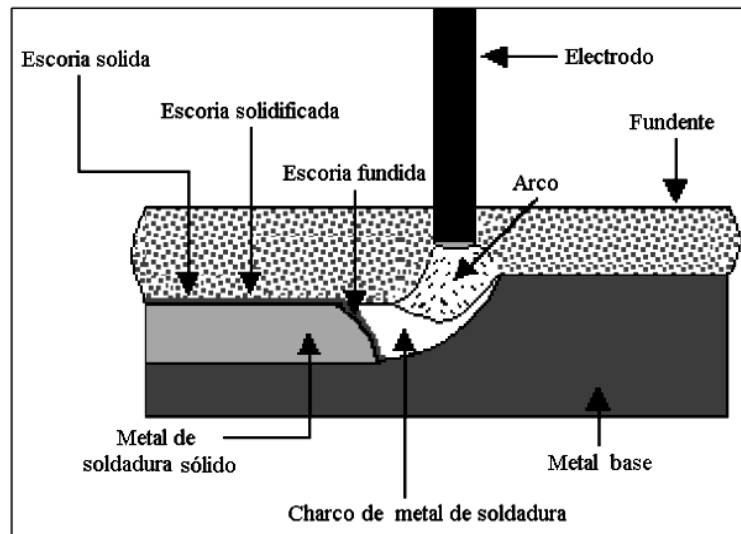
PROCESO DE SOLDADURA SAW (11)
